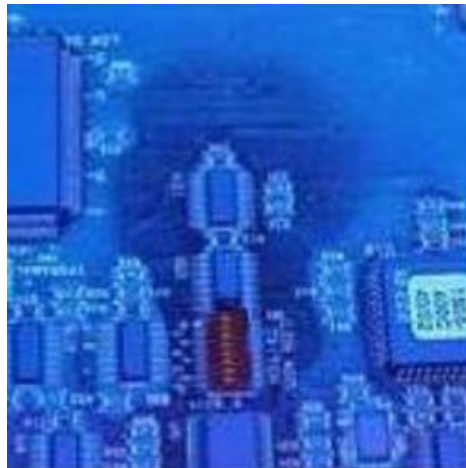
Ukázka pěny pod UV inspekcí a děr v povlaku. Převzato z [26], [29]
